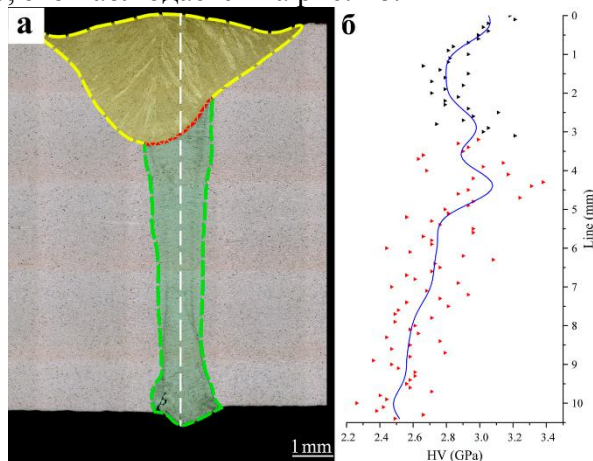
а – форма сварного шва; б – профиль микротвердости по вертикальной траектории 3
